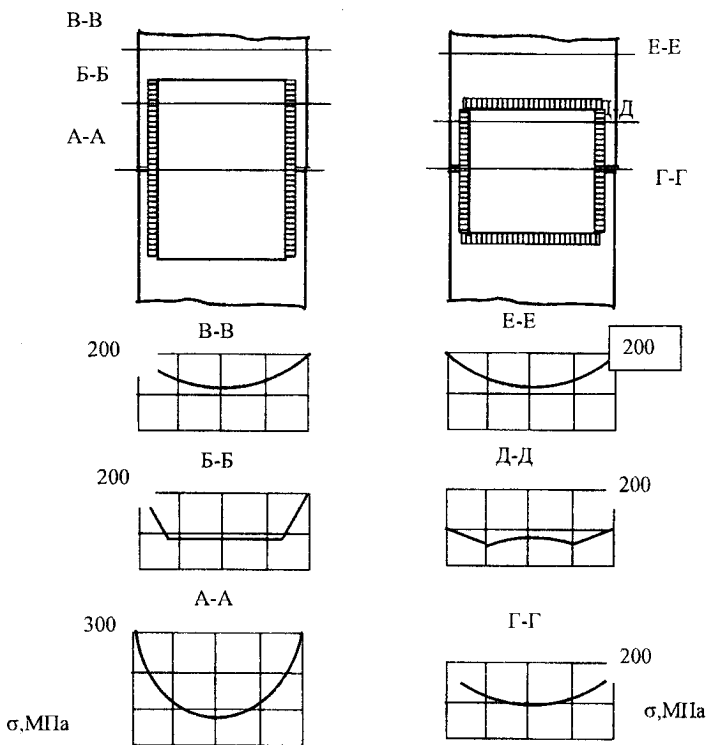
Розподіл напружень в з'єднанні з накладками
